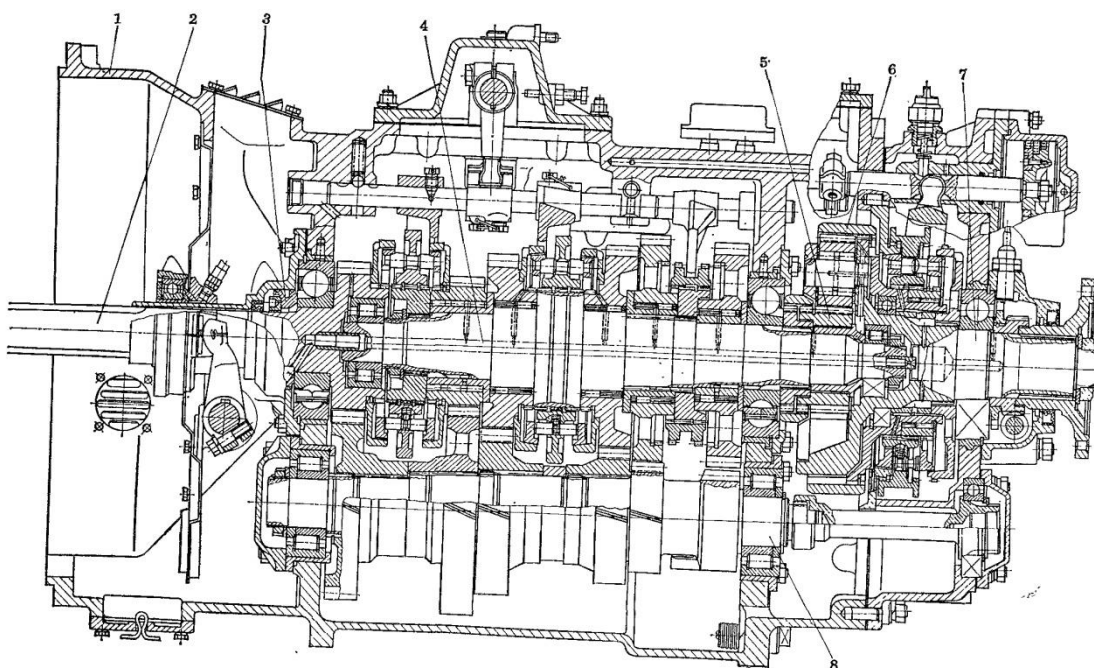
9-ступенчатая коробка передач ЯМЗ-205
